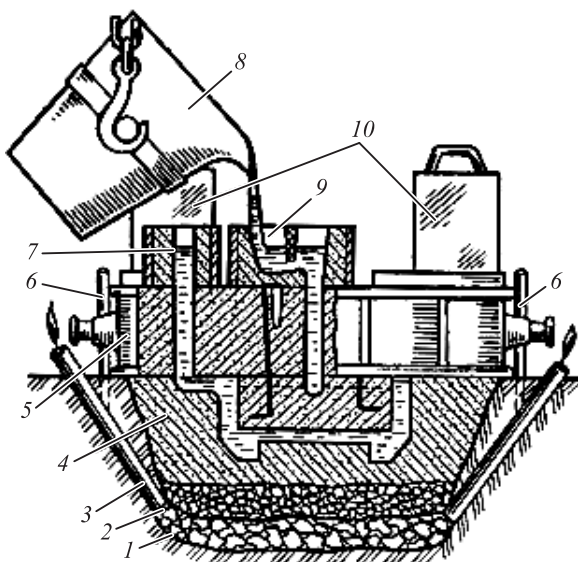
Устройство формы, изготовленной по твердой постели:
